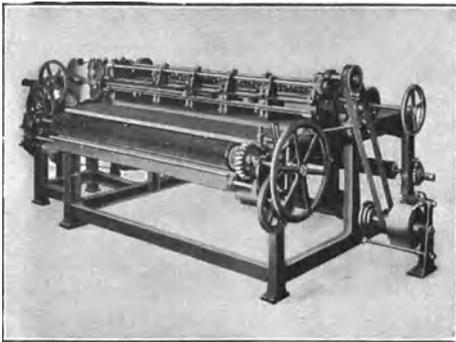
Wirbelmaschine mit seitwärts bewegbaren, um senkrechte Achsen sich drehenden Bürsten. (Otto Pieron, Abt. Rudolph & Kühne, Berlin-Bocholt.)
